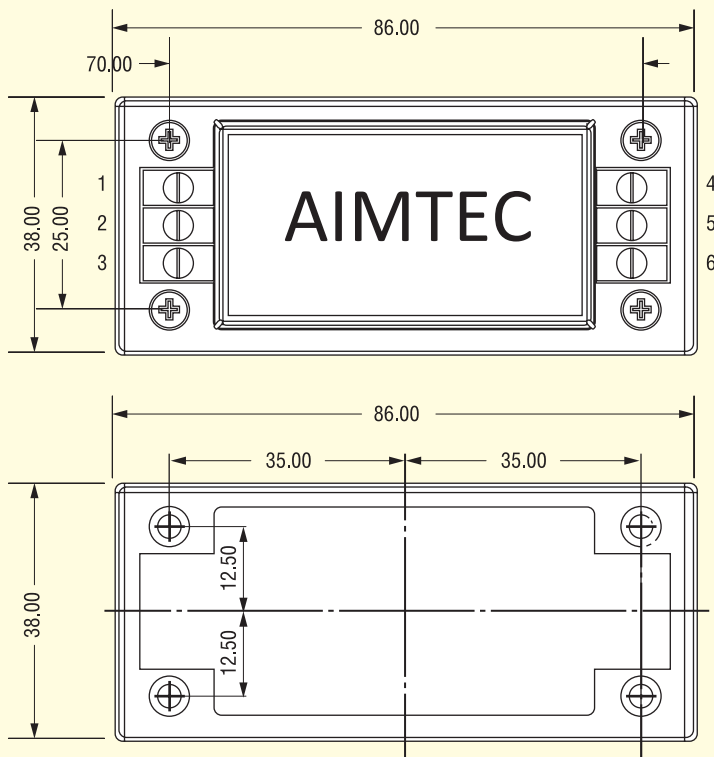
Конструкция корпуса AC/DC конвертера для установки на шасси
